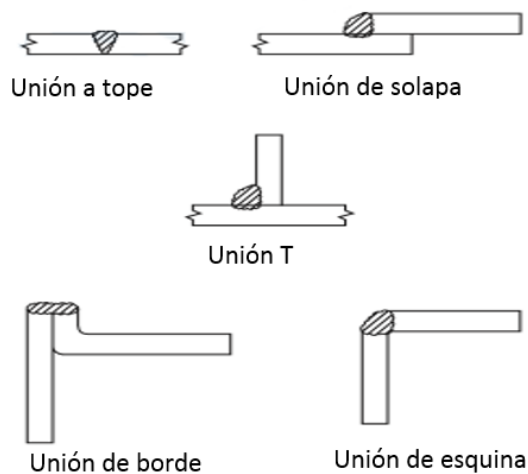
Uniones básicas en los procesos de soldadura (24).
